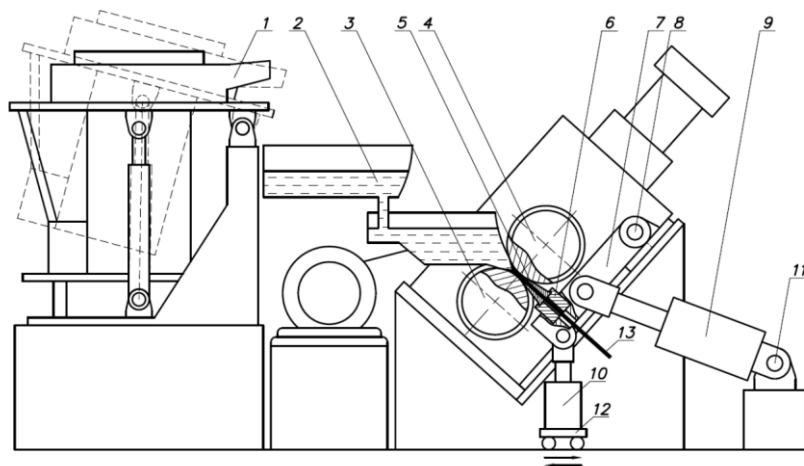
Общий вид установки СЛиПП-2,5: 1 – печь-миксер; 2 – литниковая система; 3 – валок с ручьем; 4 – валок с выступом; 5 – матрица; 6 – матрицедержатель; 7 – кронштейн; 8, 11, 12 – шарниры; 9 – наклонный гидроцилиндр; 10 – вертикальный гидроцилиндр; 13 – пресс-изделие
